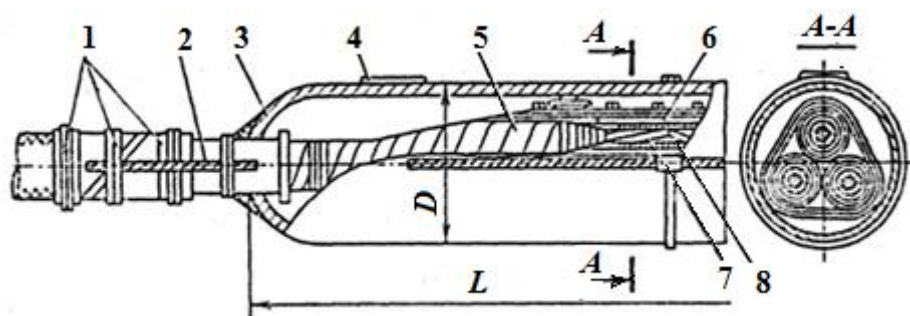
,а. Соединительная муфта в свинцовом корпусе для кабелей на напряжение 6, 10 кВ: 1 – бандаж; 2 – заземляющий провод; 3 – корпус муфты; 4 – заливочное отверстие; 5 – изоляция кабеля; 6 – подмотка из бумажных лент; 7 – токопроводящая жила; 8 – соединительная гильза
